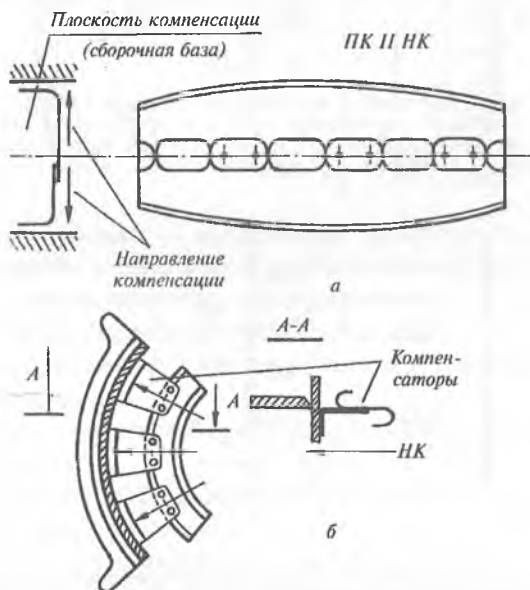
Схема сборки с компенсацией: а — сборка нервюр из полунервюр; б — скрепление обшивки и шпангоута при помощи деталей компенсаторов
